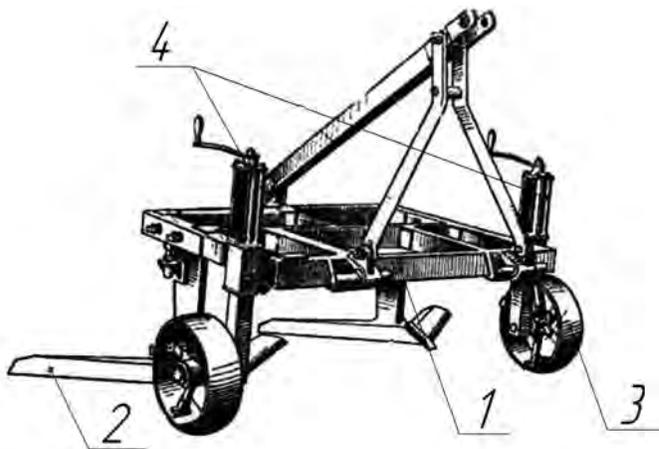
Общий вид культиватора-глубококорыхлителя:
